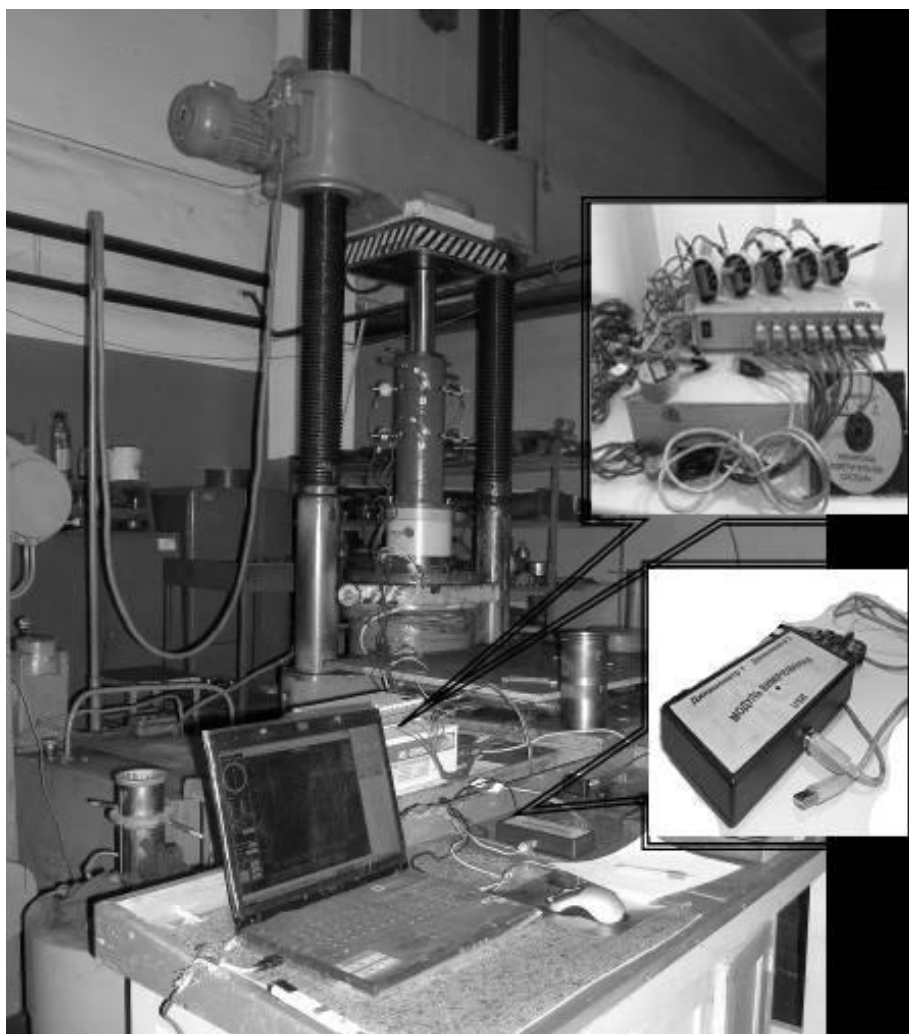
Исследовательский стенд для изучения процесса комбинированного протягивания
